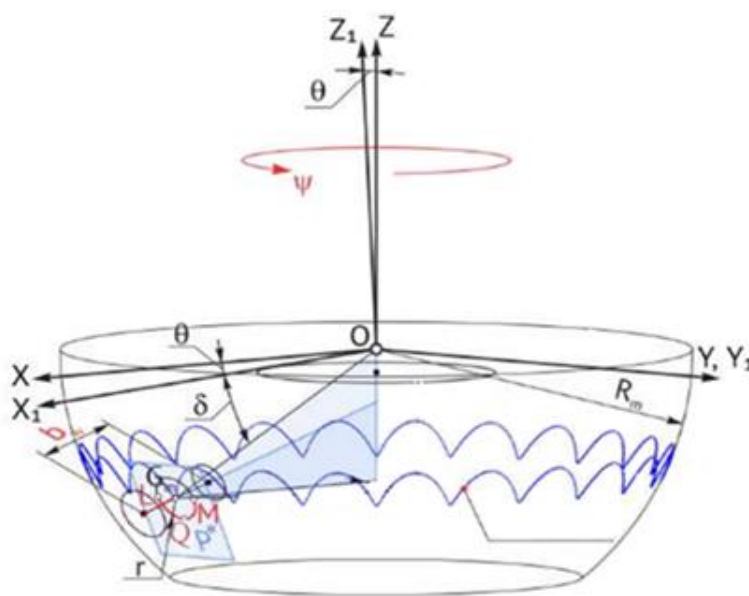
Описание сферического движения блока шестерен волнового торцевого кинематического редуктора
